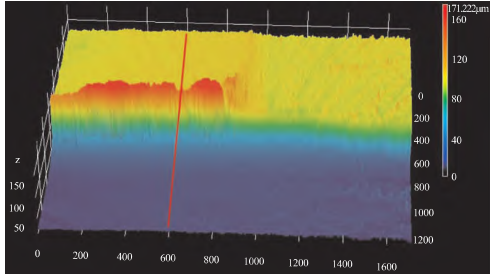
金属加工件表面(工件尺寸 10mm $\times$ 20mm)
